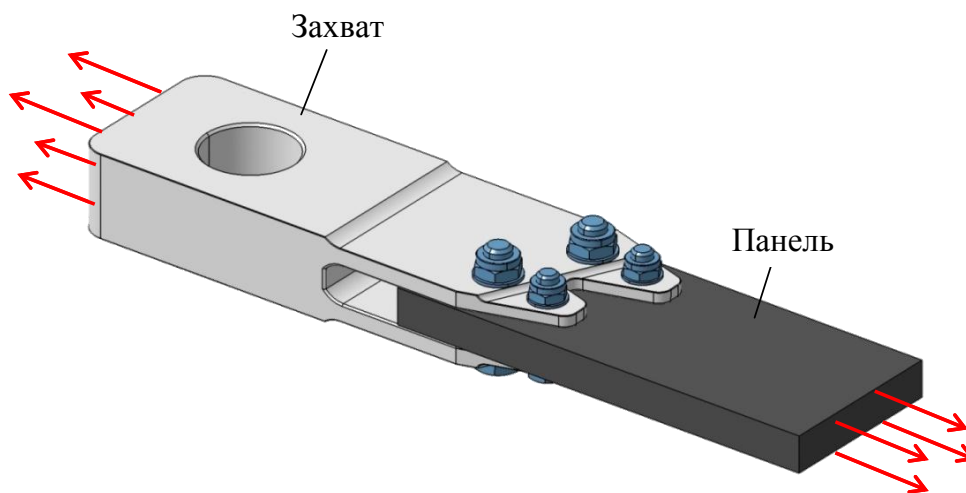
Конструкция агрегатов из ПКМ
